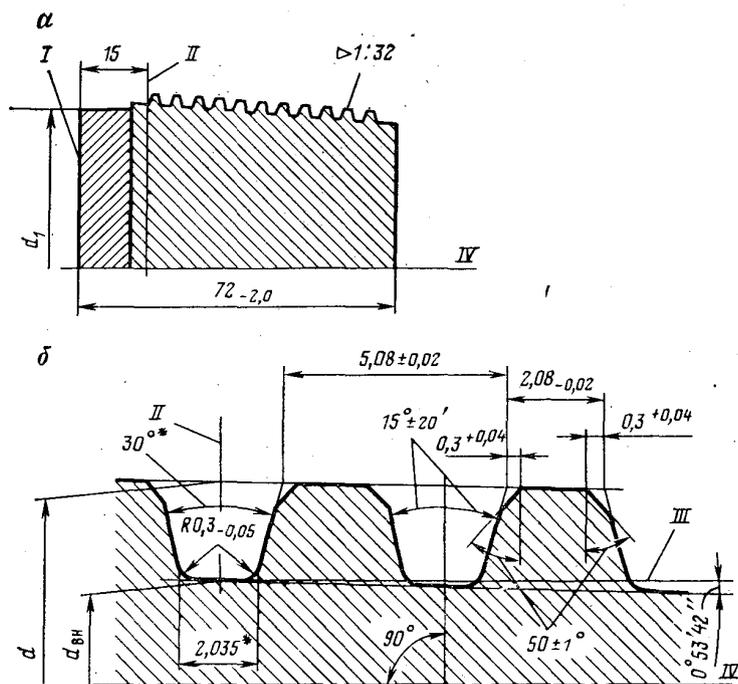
Калибр-пробка Р (а) и его профиль (б) для контроля резьбы ТТ:
